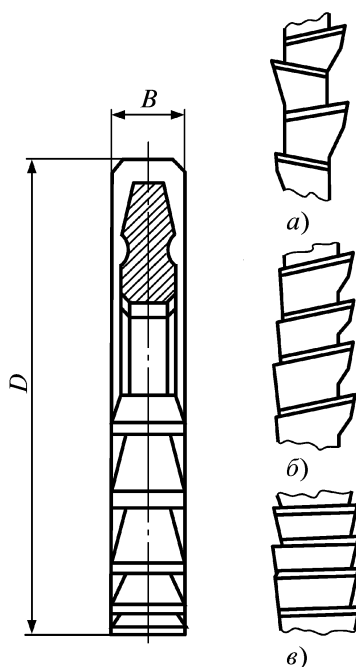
Схемы расположения зубьев дисковых фрез
